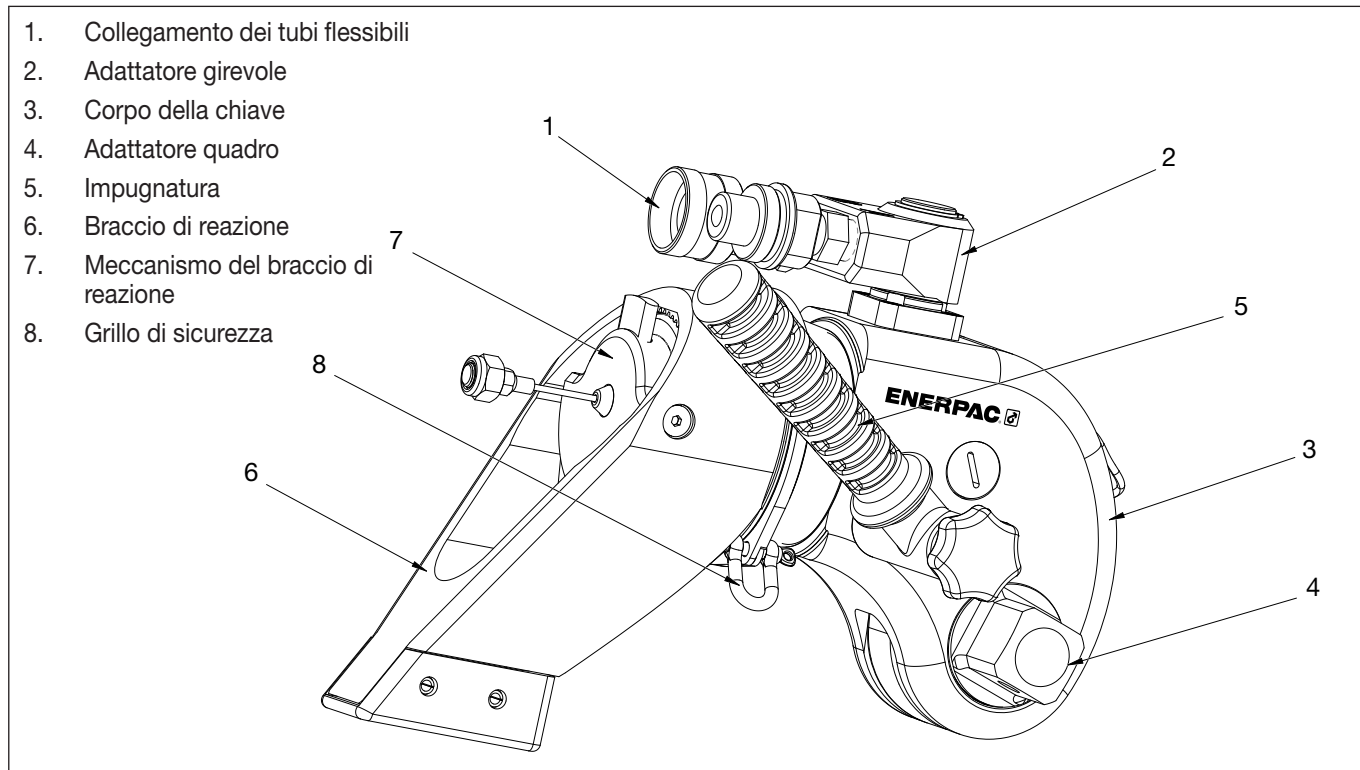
Funzioni e componenti principali della Chiave Dinamometrica DSX
